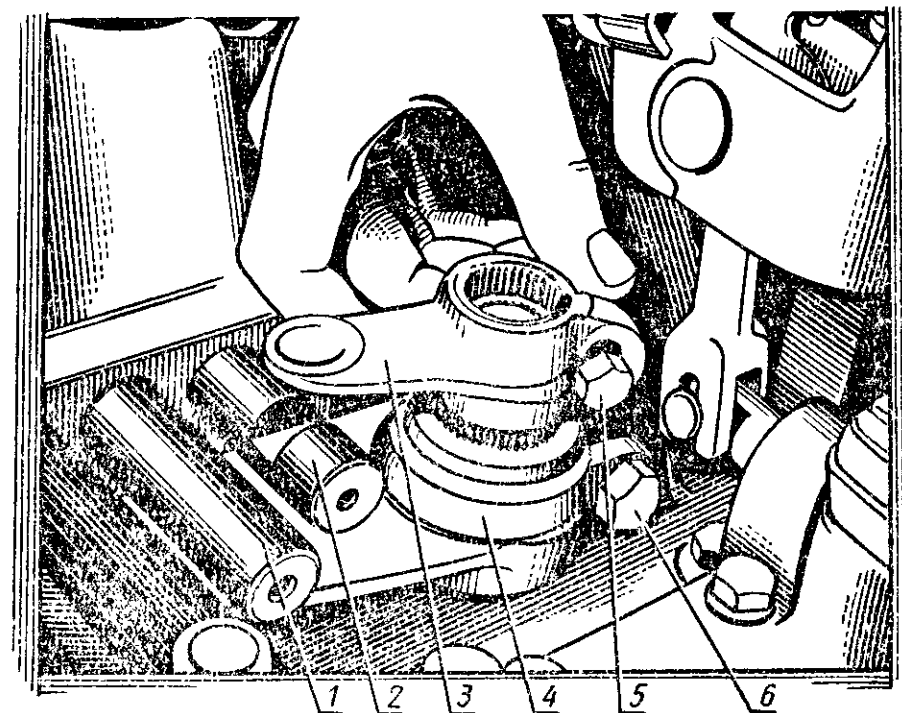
Регулировка привода управления зубчатыми муфтами грузового вала и заднего хода:
